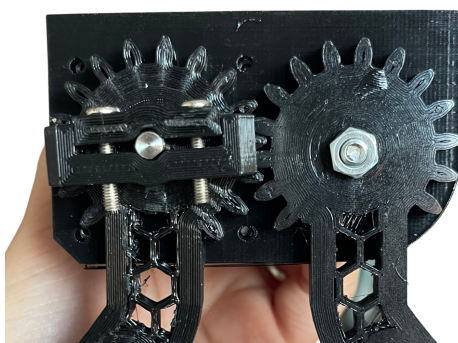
Protótipo da garra mecânica impressa em 3D, montada com o motor - Encaixe das engrenagens.
